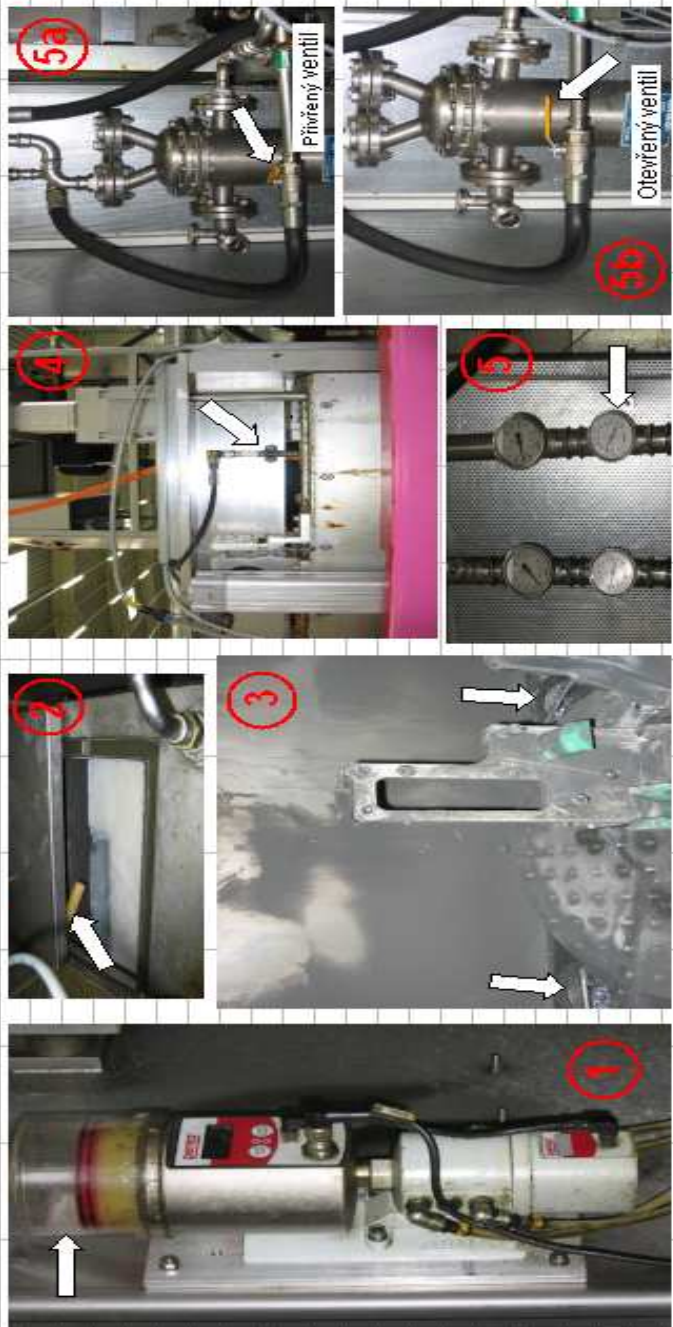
Standard samostatné inspekční prohlídky stroje SW BAW 06 [vlastní]
